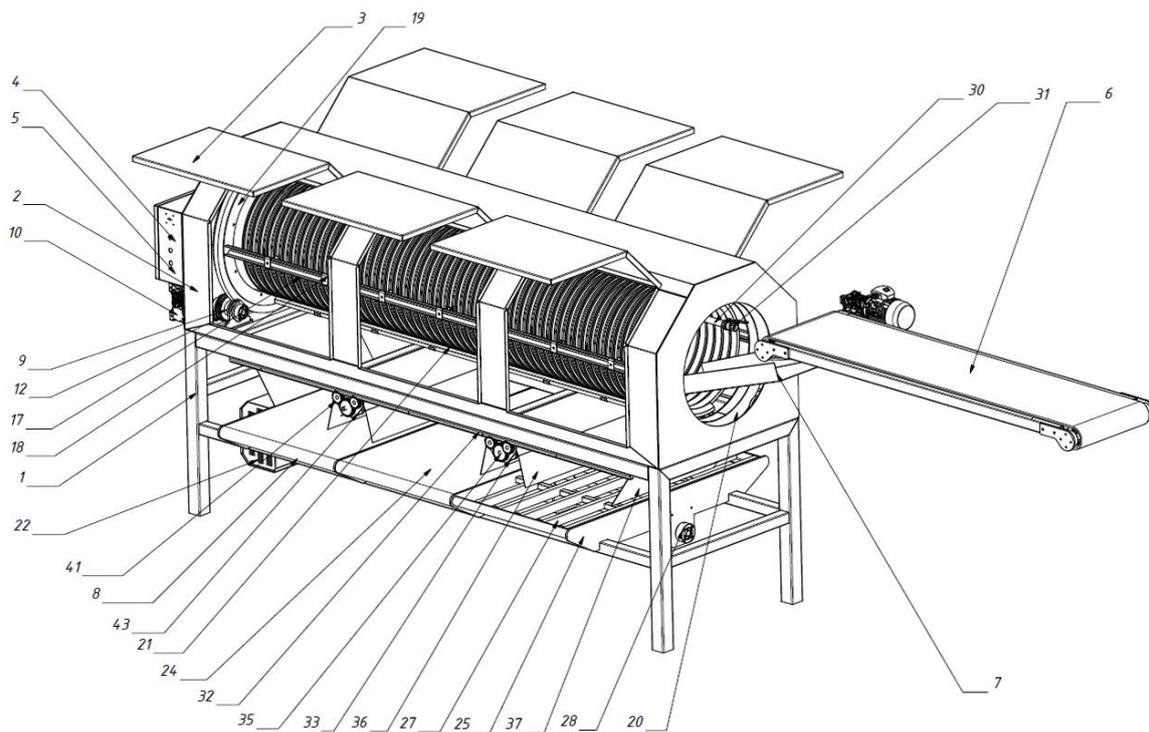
Схема машины для сортировки рыбы, общий вид
